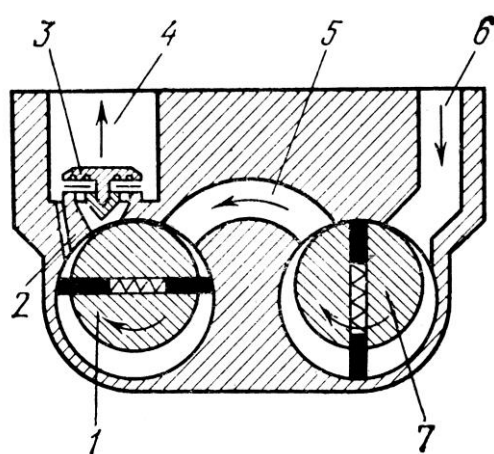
Схематическое устройство двухступенчатого пластинчато-роторного насоса: 1, 7 — роторы; 2 — дроссельное отверстие; 3 — клапан; 4 — выпускной патрубок; 5 — соединительный канал; 6 — входной патрубок
